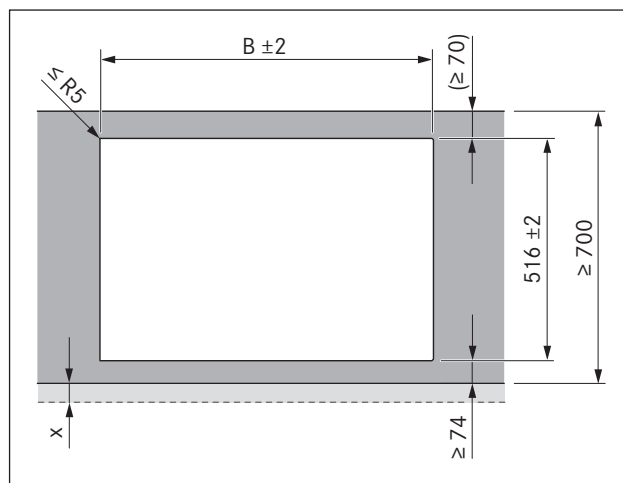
Rozmery drážky pre zapustenú montáž
